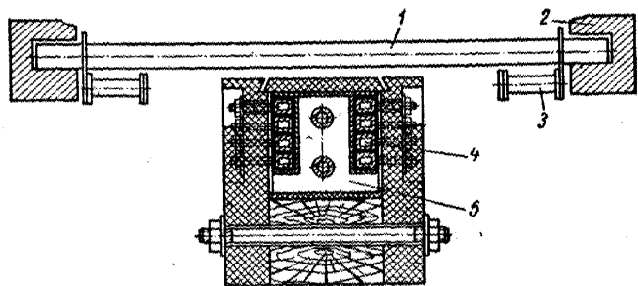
Схема нагревателя для местного нагрева прямоугольных заготовок:
